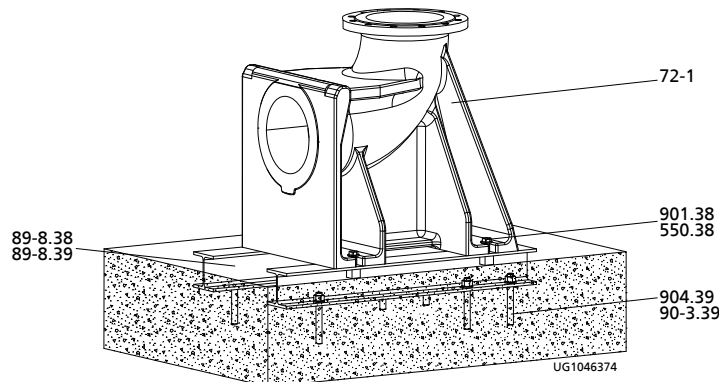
Крепление фланцевого колена с лапой с помощью фундаментных направляющих и соединительных анкеров
